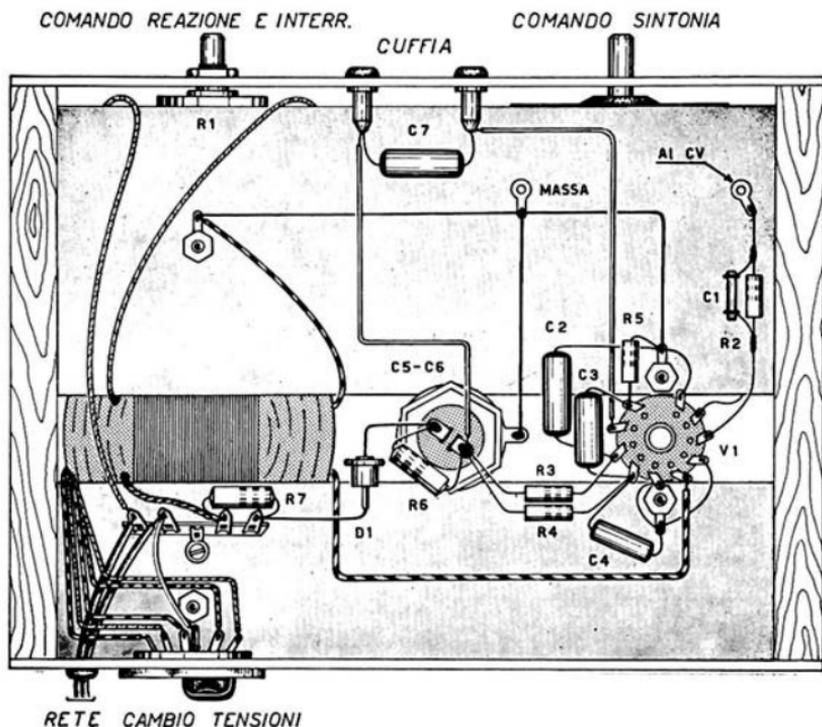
Componenti e collegamenti sotto il telaio.
